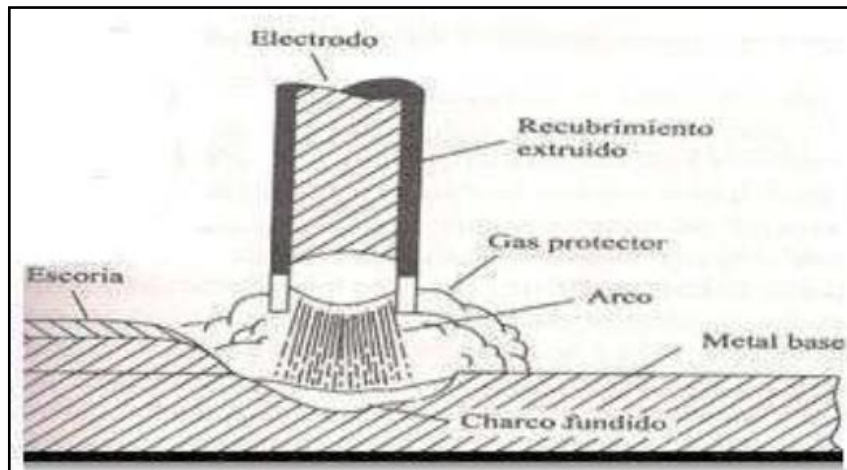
Elementos del proceso de soldadura por arco eléctrico.
